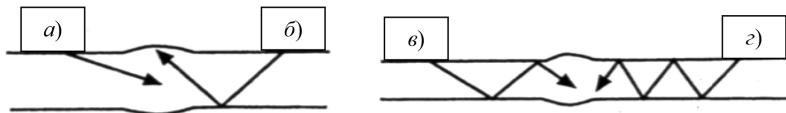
Схемы прозвучивания стыковых сварных соединений эхо-методом: а — прямыми лучами; б — однажды отраженными лучами; в — дважды отраженными лучами; г — многократно отраженными лучами
